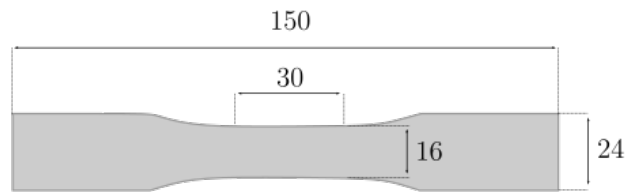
Dimensions en millimètres des éprouvettes haltères utilisées au cours de cette étude
